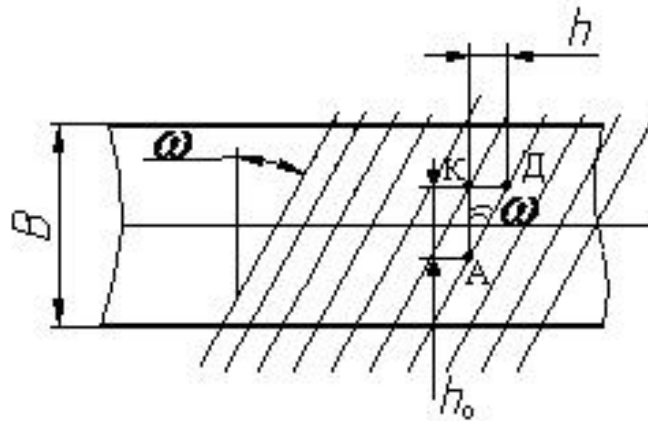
Развёртка цилиндрической поверхности косозубой фрезы на площадь её контакта с заготовкой
